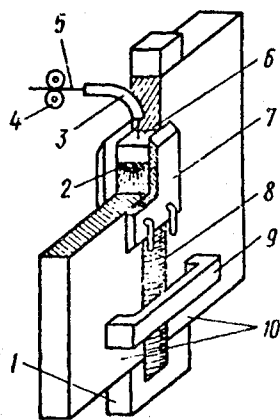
Электрошлаковая сварка: 1 — начальная скоба для возбуждения процесса сварки; 2 — металлическая (сварочная) ванна; 3 — токоподводящий мундштук; 4 — подающие ролики; 5 — электродная проволока; 6 — шлаковая ванна; 7 — медные формующие ползуны; 8 — сварной шов; 9 — сборочная скоба; 10 — свариваемые детали
